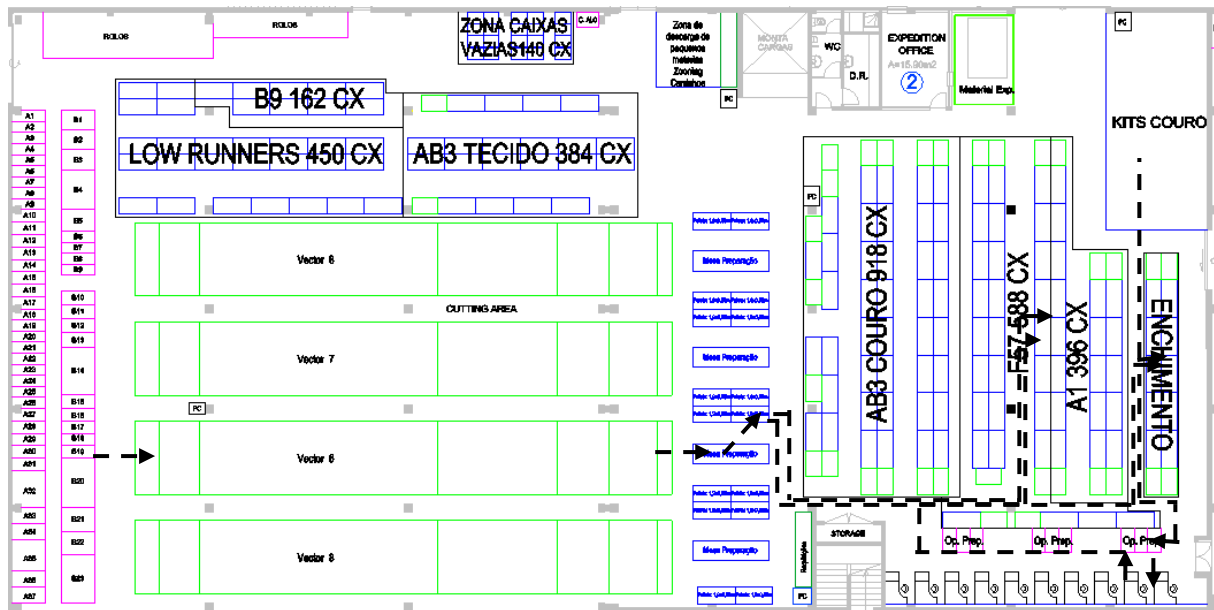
Primeira proposta layout - fluxo projeto Mini F57 c/enchimento
